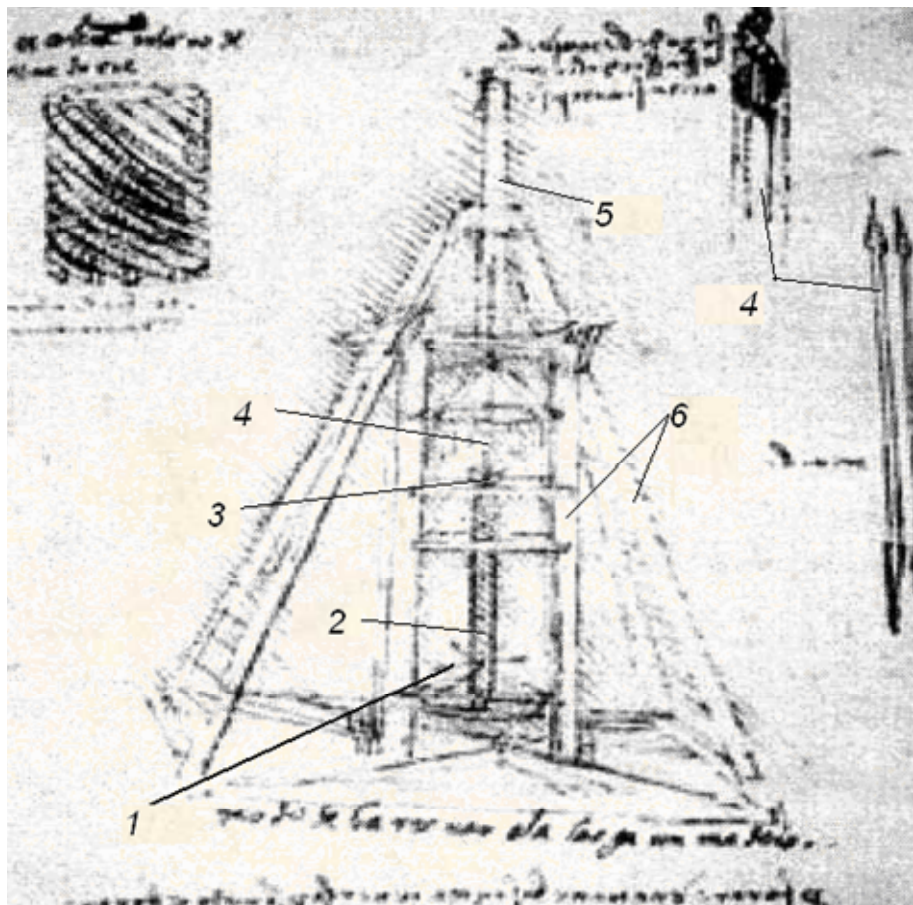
Сверлильный станок с гидромеханическим приводом:
